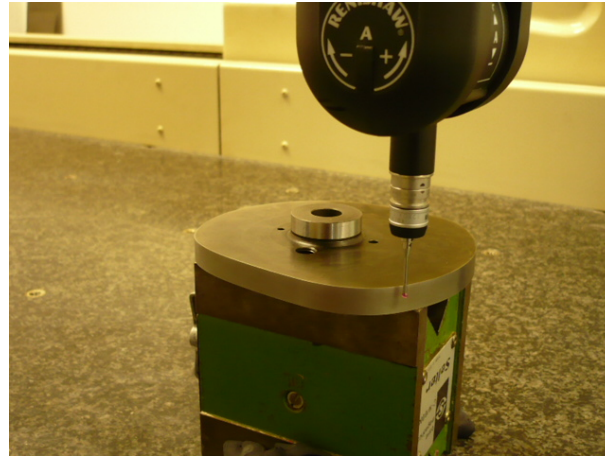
Mesura dels errors de fabricació del perfil de la lleva conjugada del primer conjunt amb la màquina de CMM
